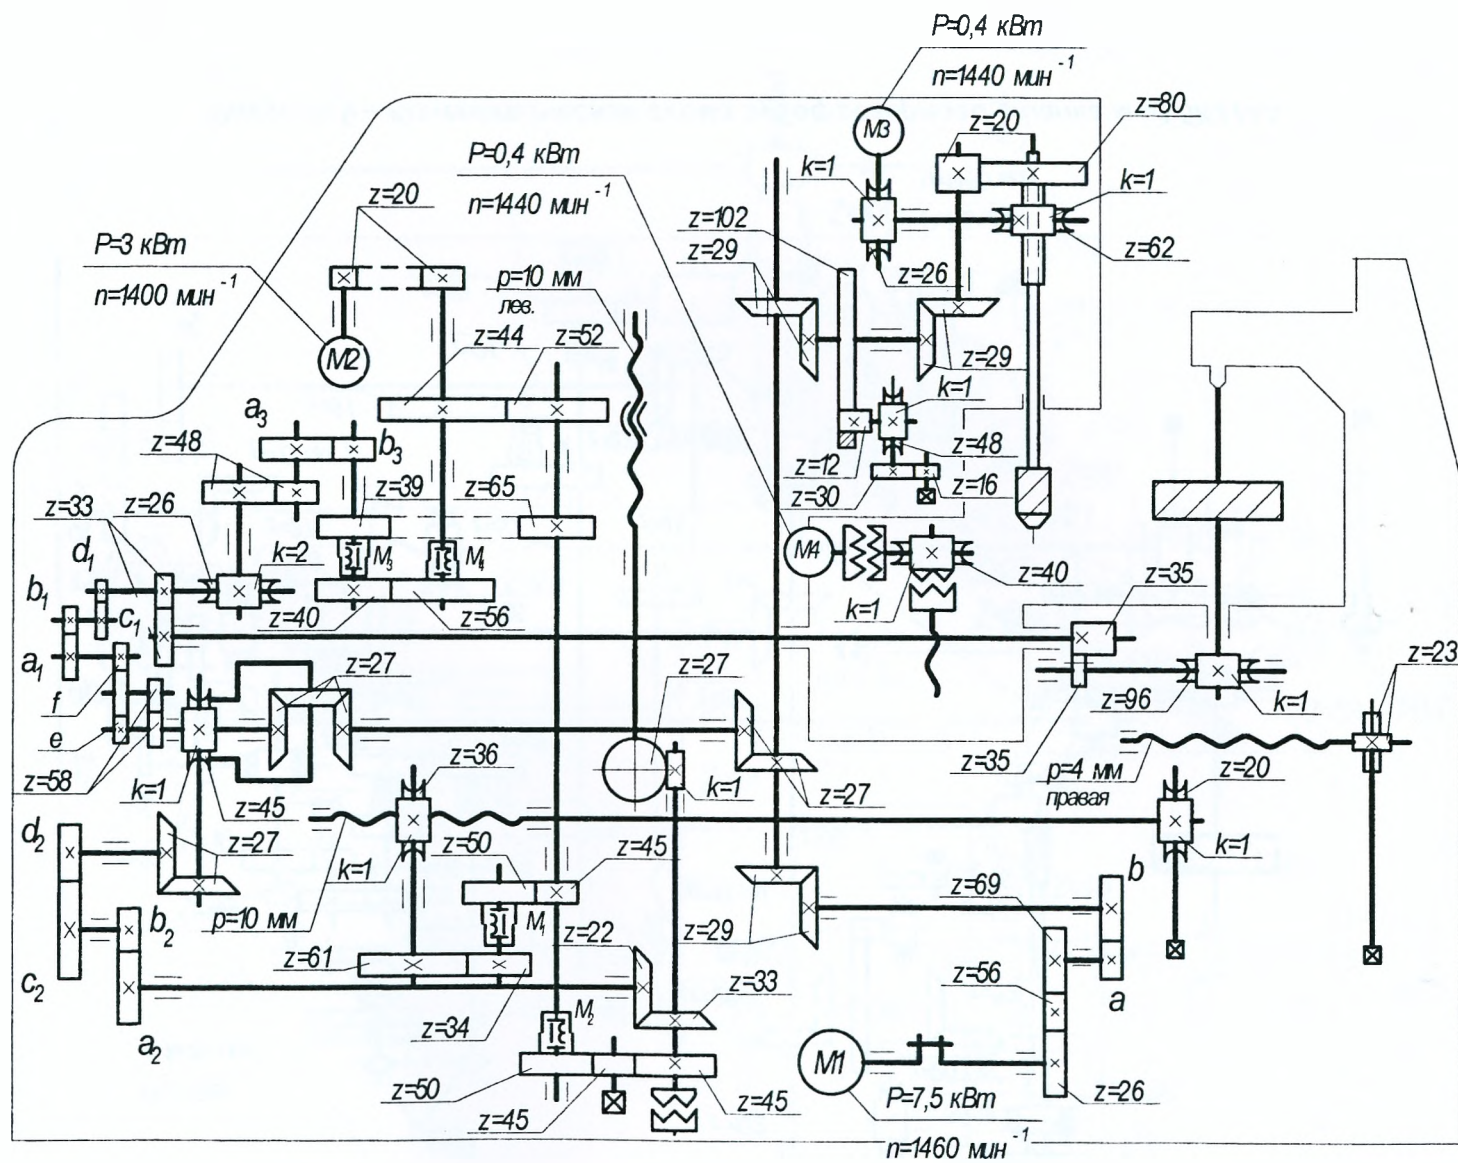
Кинематическая схема зубофрезерного станка мод.5М324А
